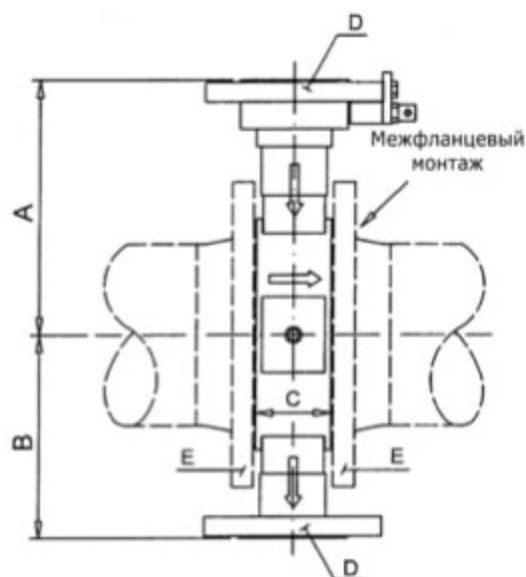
Дозаторы TP/ TPW-100/50, 150/50, 200/80, 250/80 (старый тип). Способ установки и габаритные размеры изделий.
